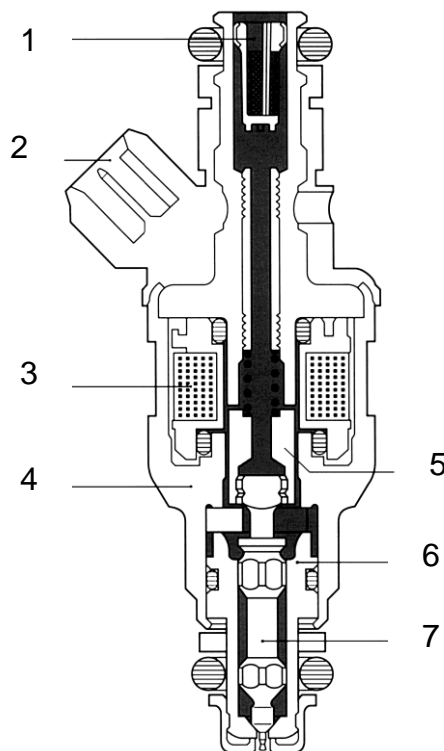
Электромагнитная форсунка (ЭМФ): 1 - фильтр топлива; 2 - соединительный разъем; 3 - катушка электромагнита; 4 - корпус; 5 - сердечник; 6 - направляющая; 7 - запорная игла
